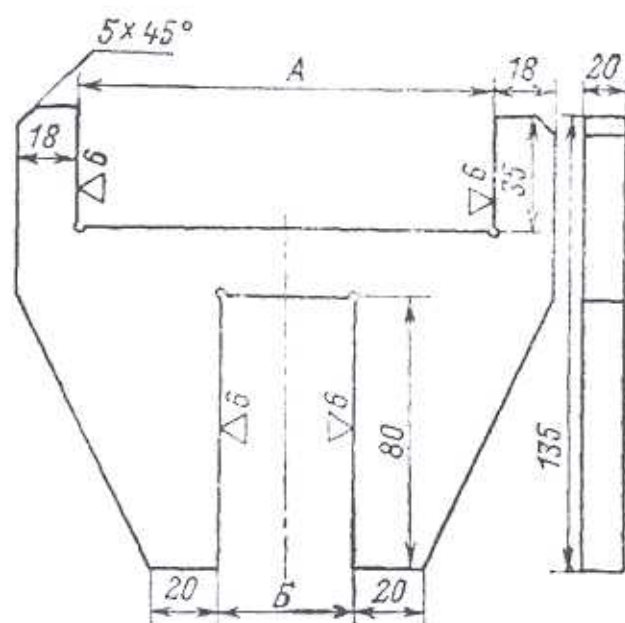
Калибр для проверки размеров изолированного стержня:
